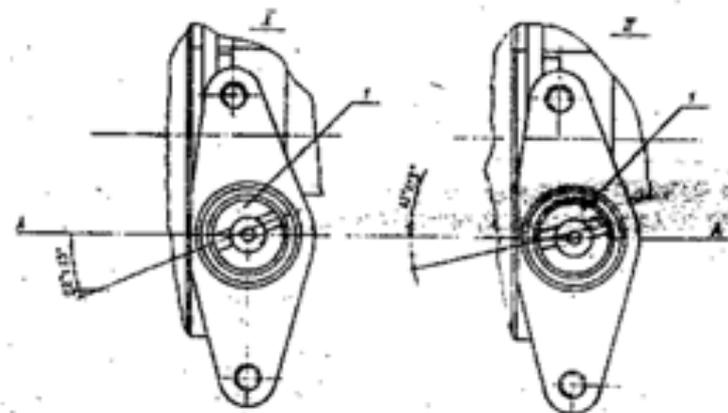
Установка ведомой шестерни привода датчика-распределителя: I - меньший сектор поводка шестерни привода; I - положение паза до установки шестерни; II - положение паза после установки шестерни; А-А - продольная ось двигателя
